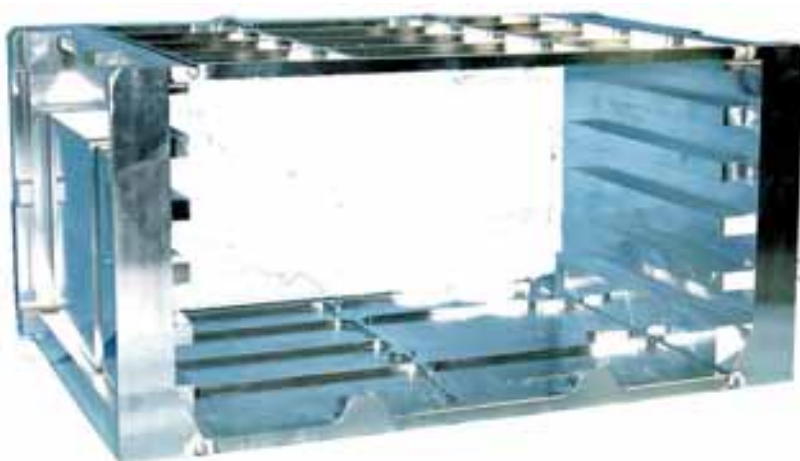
Präzisionsbaugruppe aus gefrästen Aluminiumplatten durch Elektronenstrahl-Schweißen zu einem Gehäuse gefügt.
